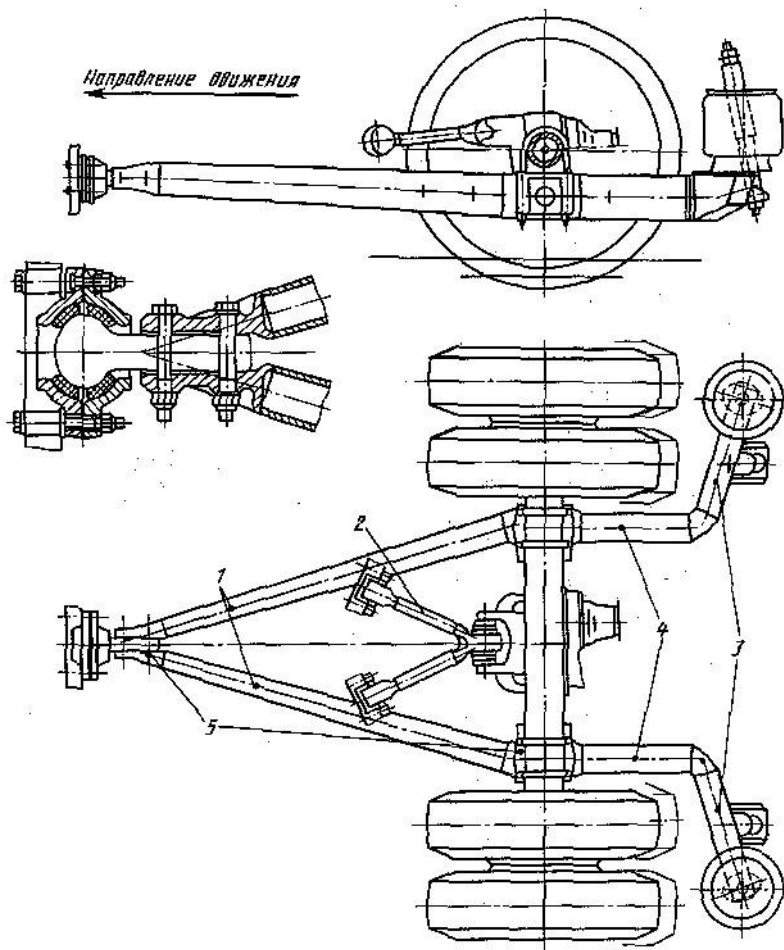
Пневматическая подвеска с дышлом задних колес автобусов МАН, с задним расположением двигателя. Каждая половина дышла представляет собой сварной узел, состоящий из штамповок и балок (полых листовых профилей). Обе половины скрепляются резьбовыми соединениями, спереди — с шаровым пальцем, а в середине — с балкой подвески; их задние консольные концы несут на себе широко расставленные пневматические диафрагменные баллоны. Расстояние между ними в 1,13 раза превышает колею, что увеличивает эффективность поддержки кузова. Продольные силы воспринимаются шарниром дышла с резиновыми вкладышами, а основная часть боковых сил — треугольным рычагом. Шарнир на балке при ходах отбоя и сжатия подвески должен перемещаться по дуге меньшего радиуса, чем определяет шарнир дышла. Возникающее рассогласование компенсируется эластичной опорой вершины треугольного рычага:
